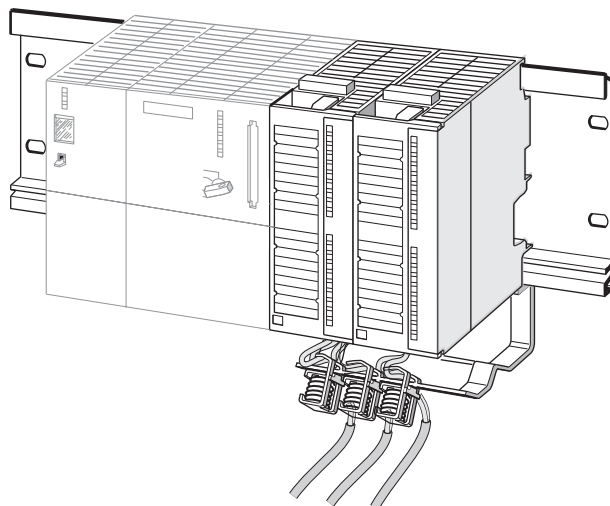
FM 350-1 con cables apantallados y con el estribo de contacto de pantalla
